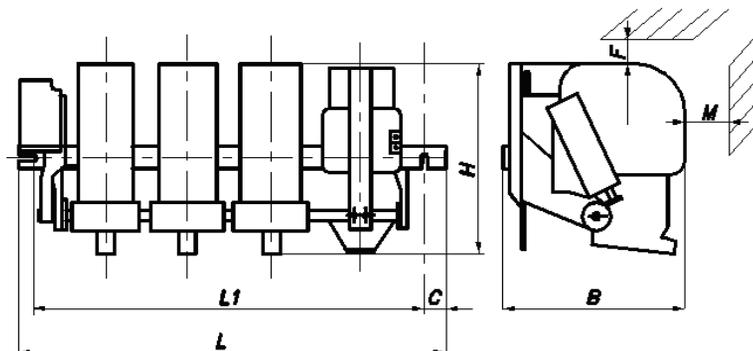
Общий вид и габаритные размеры КТ-6000.
